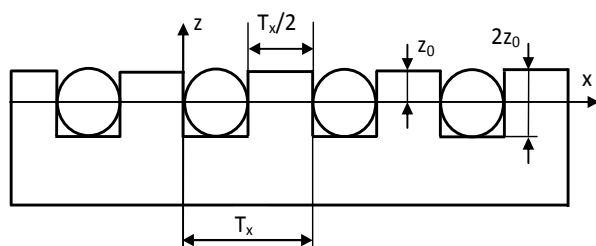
Геометрическая схема заготовки с поперечными пазы со вставками
